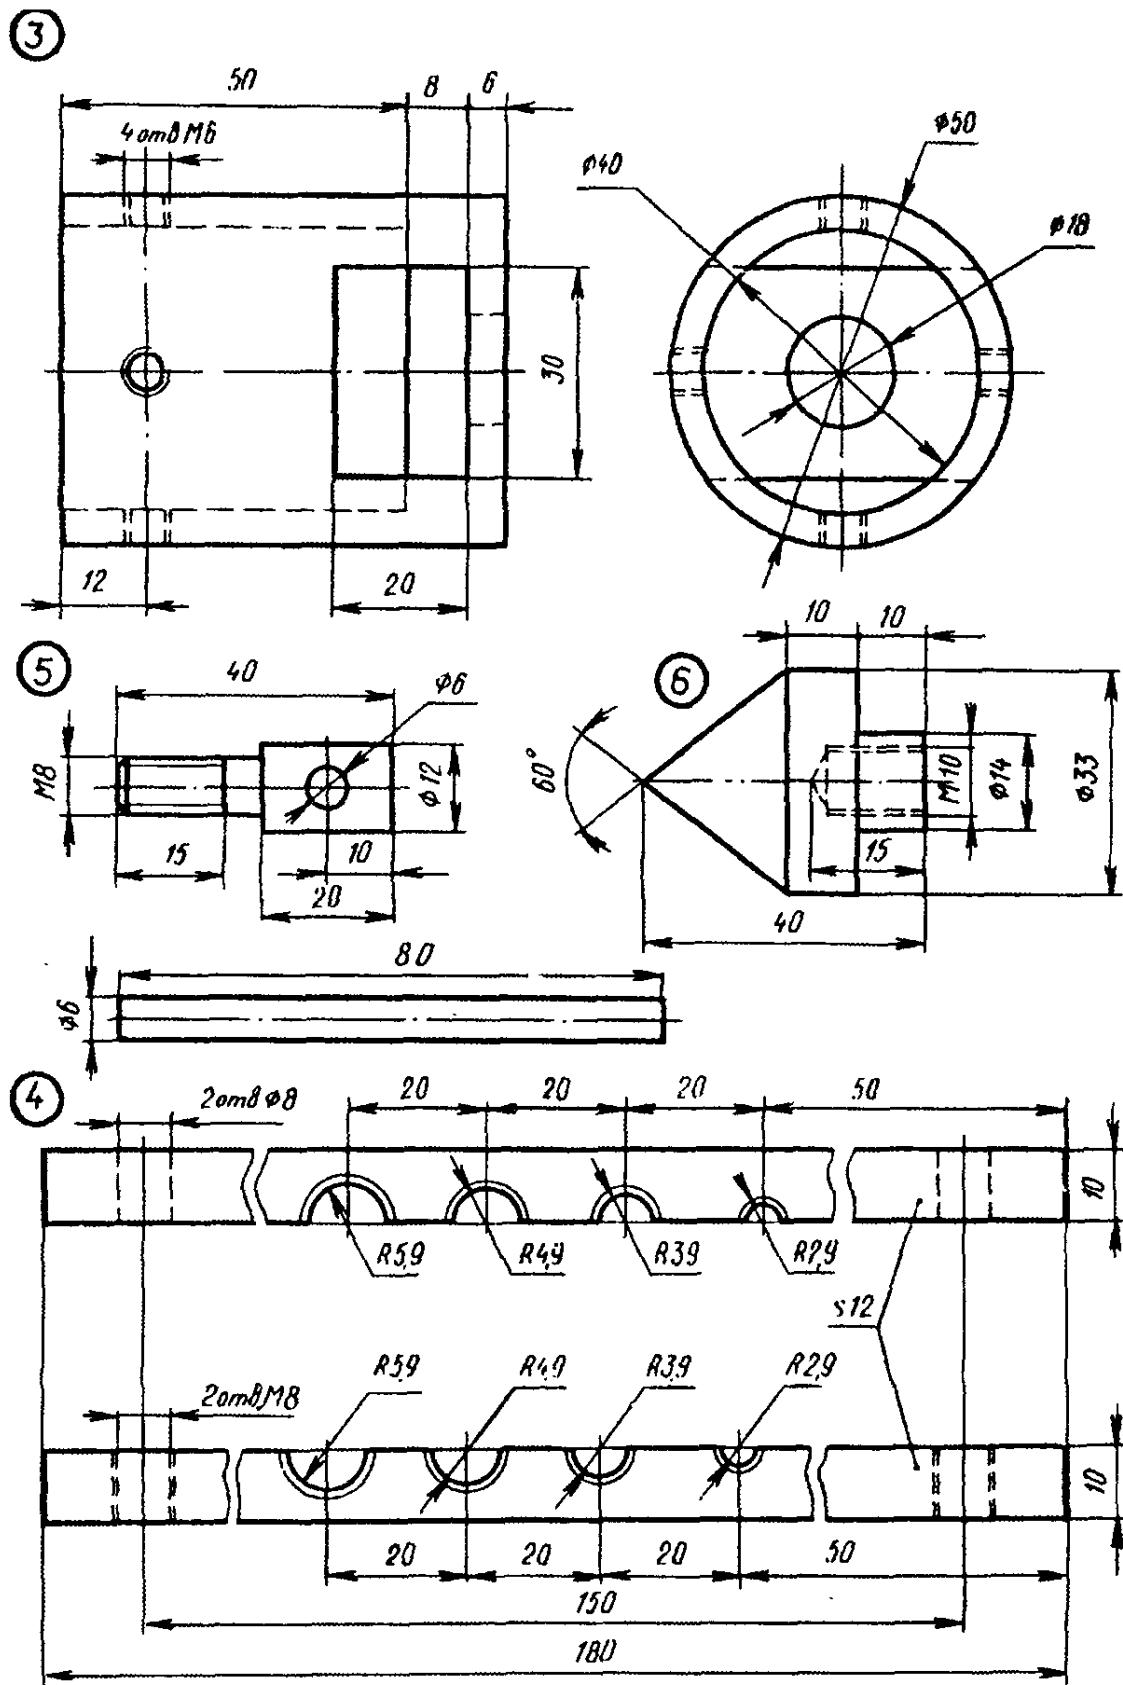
Приспособление для развалицовки трубок (продолжение).
